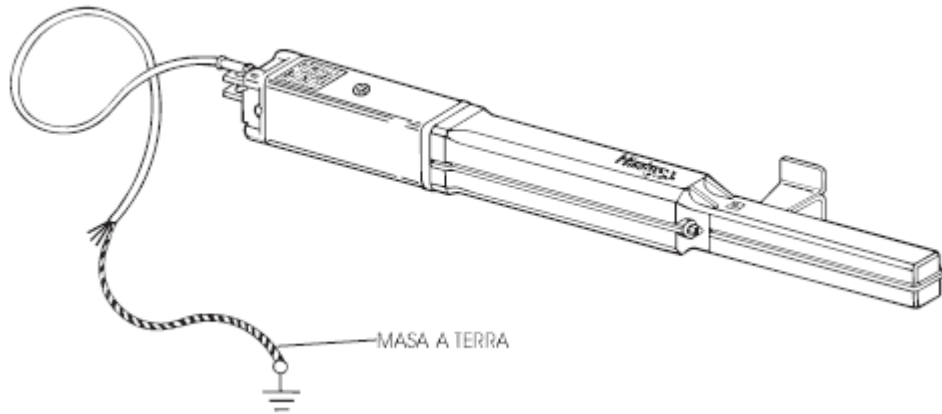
Esquema Pistón Electrohidráulico de la Máquina Ovillador
